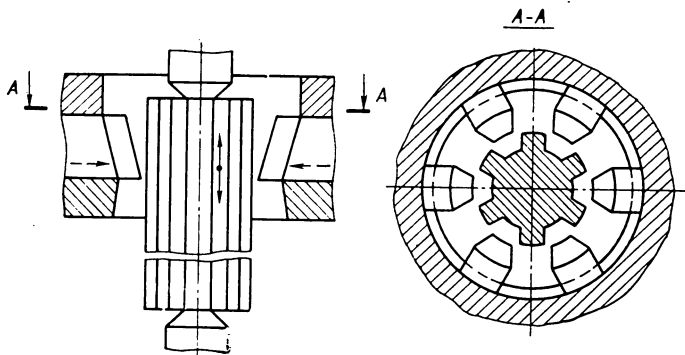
Схема одновременной обработки зубьев вала строганием много-резцовой головкой
